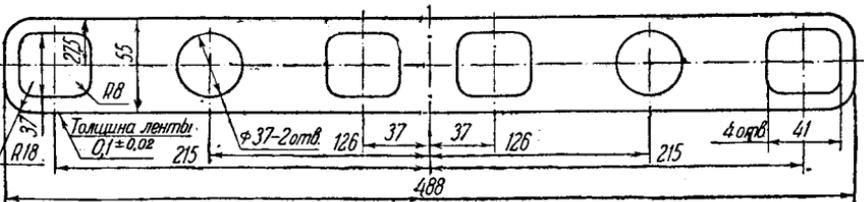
Дет. № 02-15. Лист верхний прокладки всасывающей и выхлопной труб
